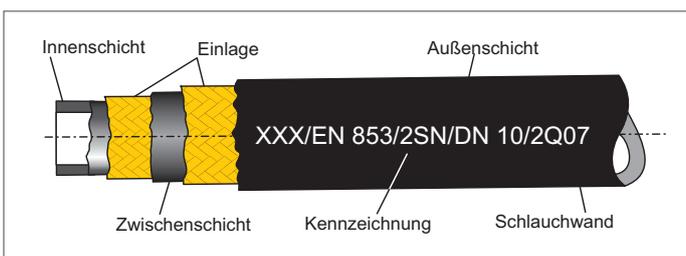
Kennzeichnung am Hydraulikschlauch
